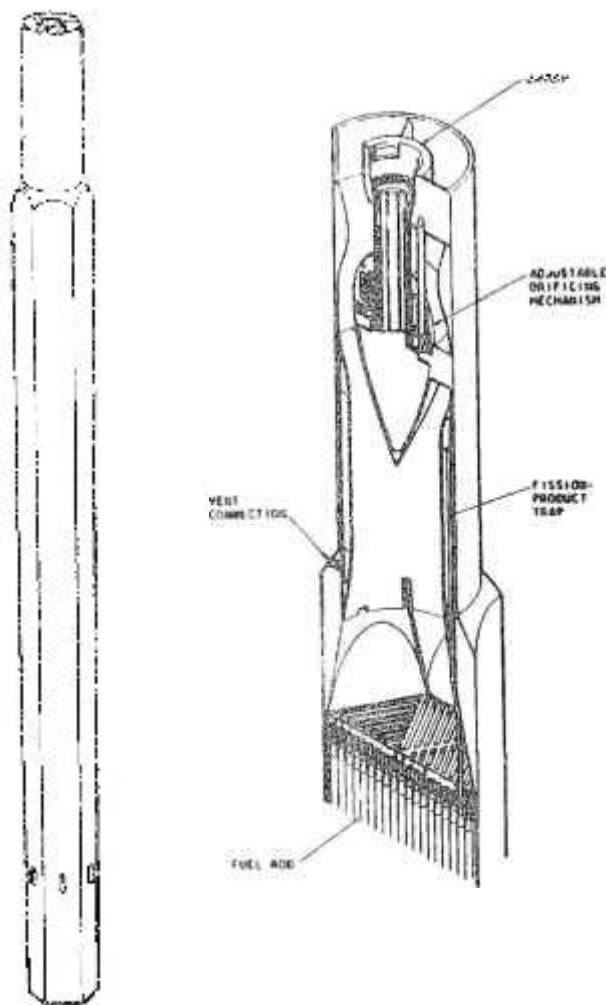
Detalhe (corte) do "Fuel Element" do GCFR
